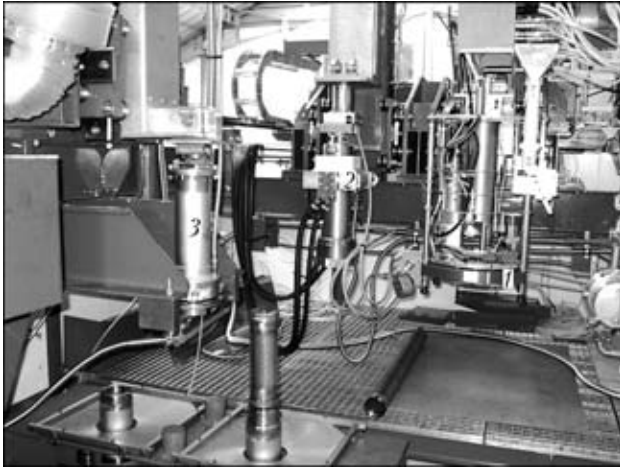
Общий вид специальной установки для приварки колпака с патроном П-89 в камере: 1 — головка для приварки колпака к патрону; 2 — головка для закачки гелия и приварки герметизации (сварки) отвода штуцера; 3 — головка для контроля патрона на непроницаемость гелием после полного цикла работ по герметизации
